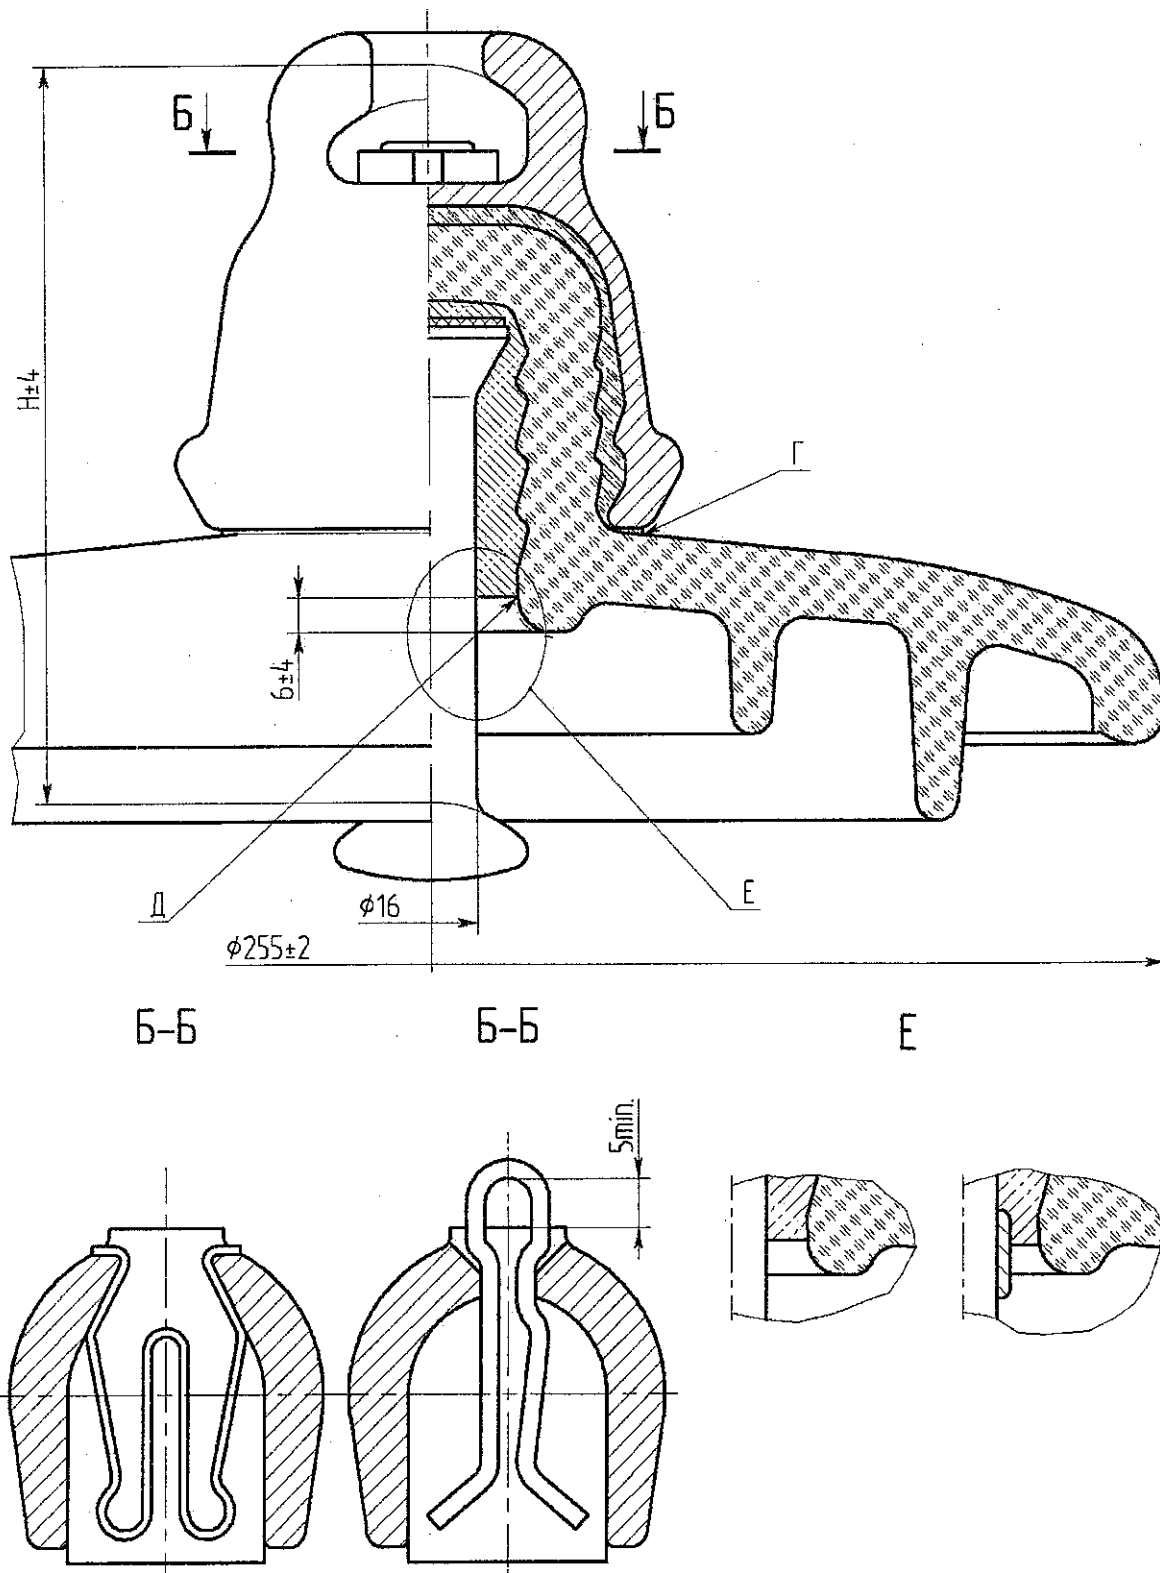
Габаритные, соединительные и установочные размеры изолятора ПС 120Б
